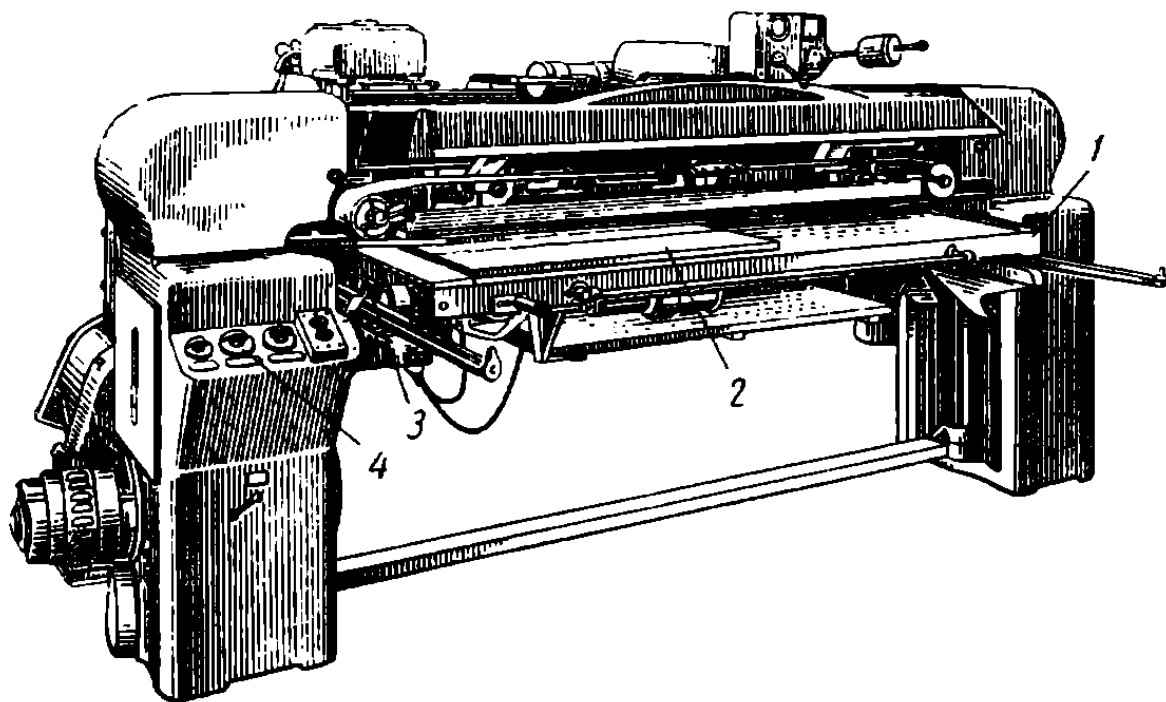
Ленточный шлифовальный станок с подвижным столом для шлифования отделочной пленки пастами:
